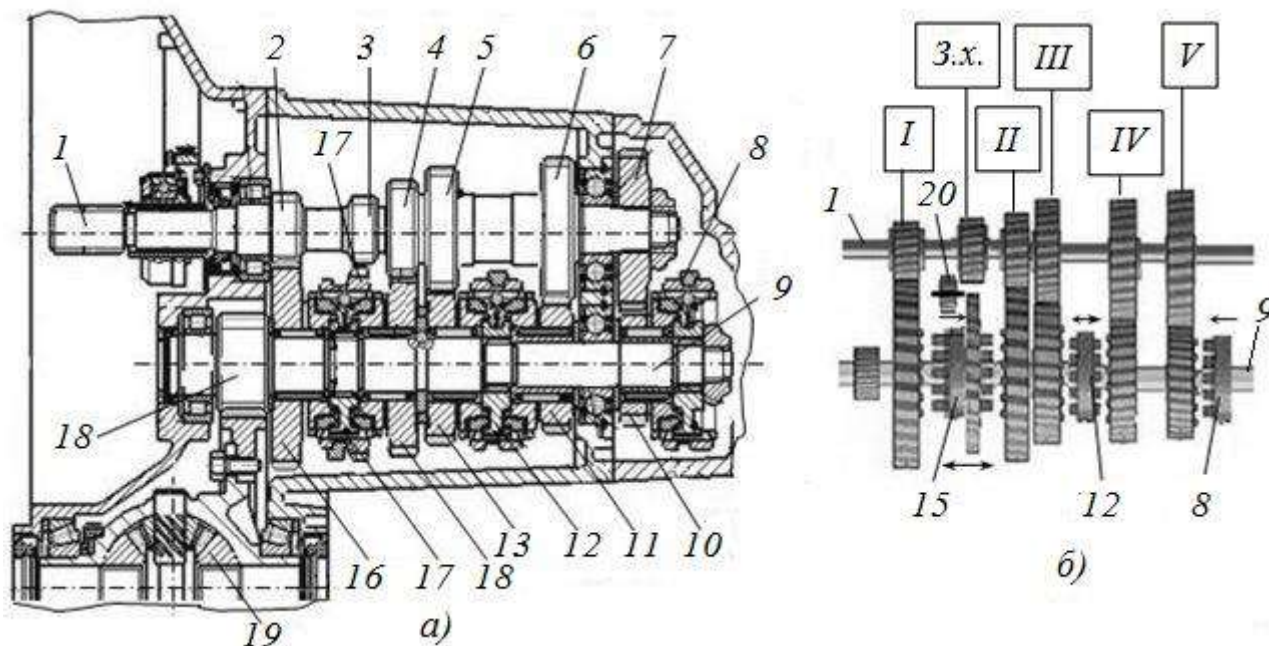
Розріз (а) та схема передач (б) двовальної коробки передач:
